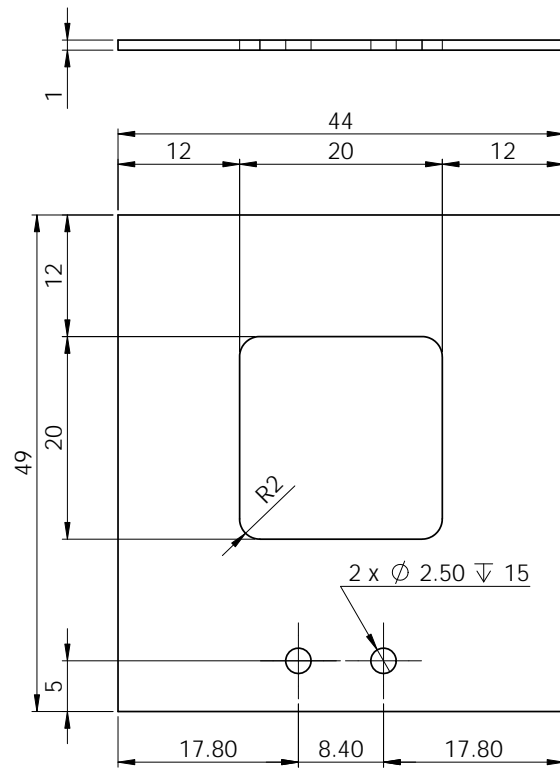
Technische Zeichnung des Probenträgers.
